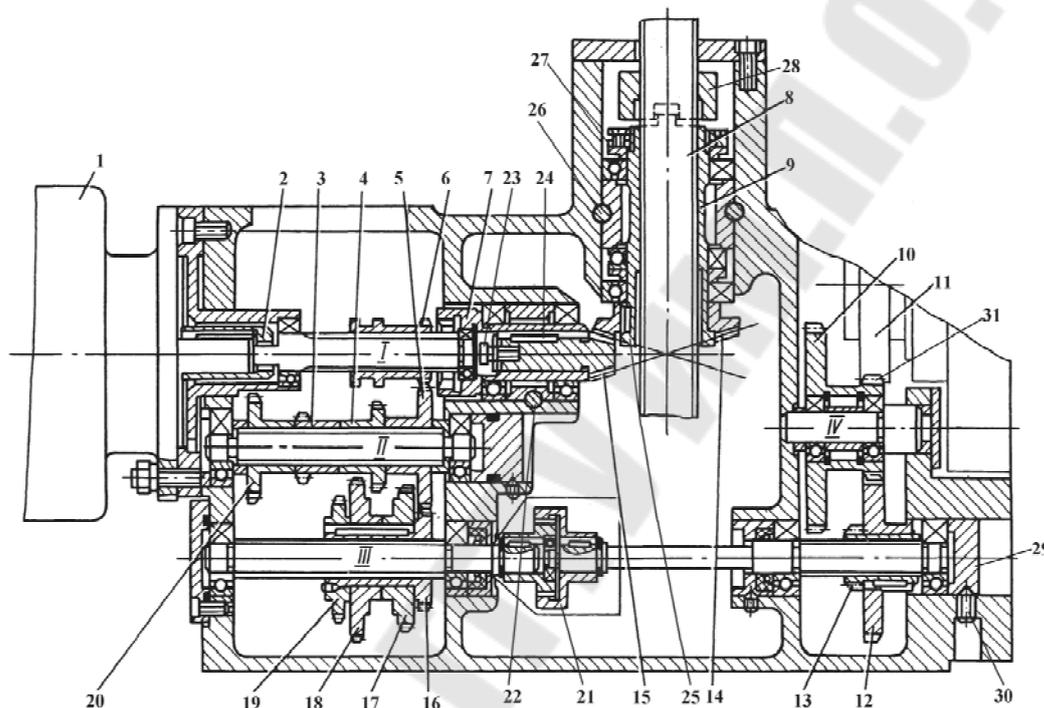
Эскиз коробки скоростей и механизма подъёма бочки
